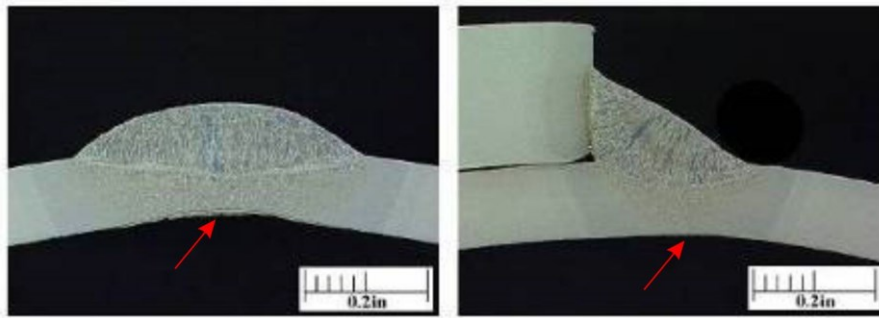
Comparação de deposição de solda. Em a) Deposição direta; b) Solda de filete de remendo. Adaptado de [84].
